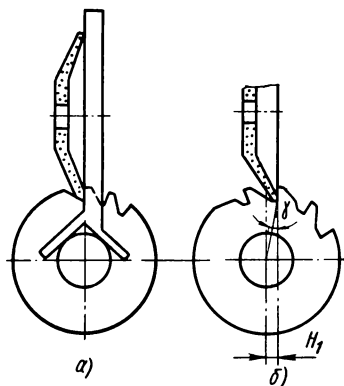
Установка фрезы при заточке передней поверхности зуба тарельчатым кругом
